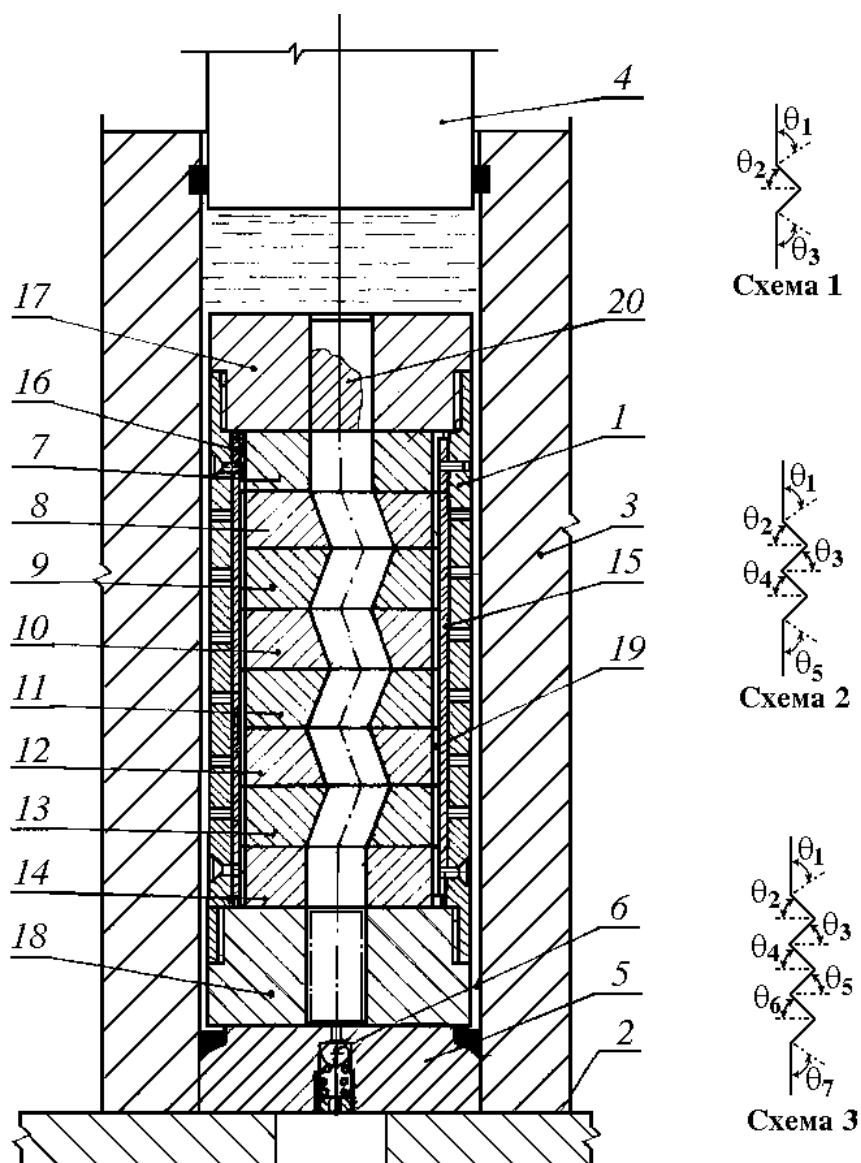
Деформирующий блок и схемные варианты его выполнения: 1 – компакт-блок; 2 – траверза пресса; 3 – контейнер; 4 – пуансон; 5 – матрицедержатель; 6 – перепускной клапан; 7–14 – втулки; 15, 16 – шпонки; 17, 18 – опорные элементы; 19 – шпоночный паз; 20 – заготовка
